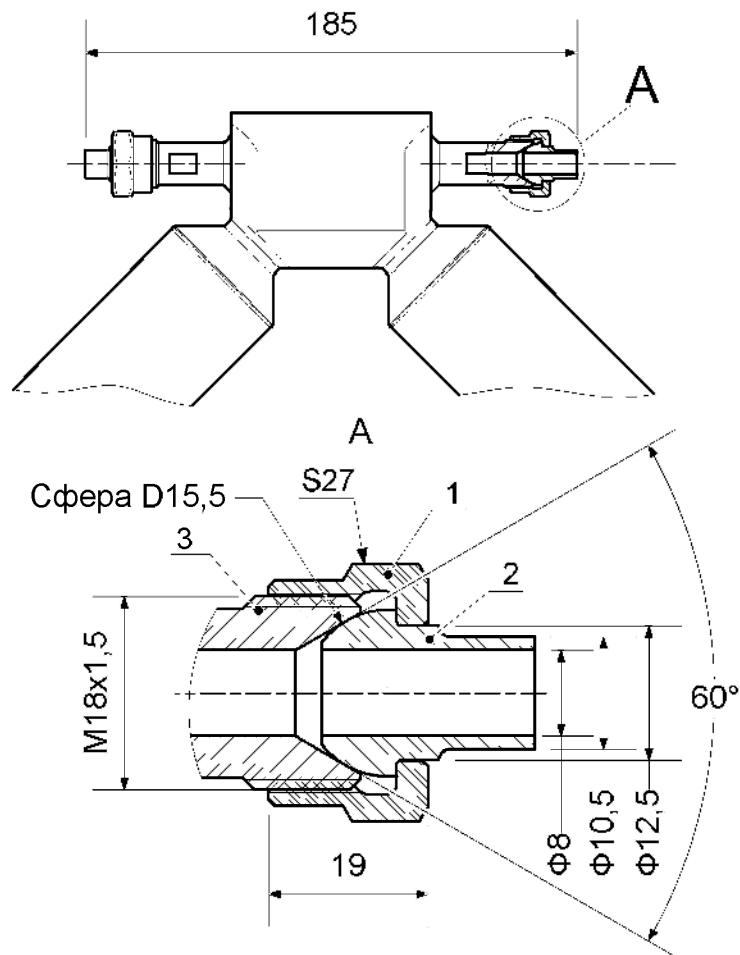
Монтаж датчика ТИ-0045 с резьбовым присоединением
